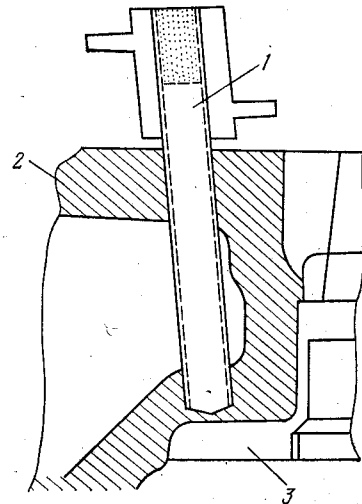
Охлаждение кокиля с помощью тепловой трубы: 1 — тепловая труба; 2 — корпус кокиля; 3 — расплавленный металл
